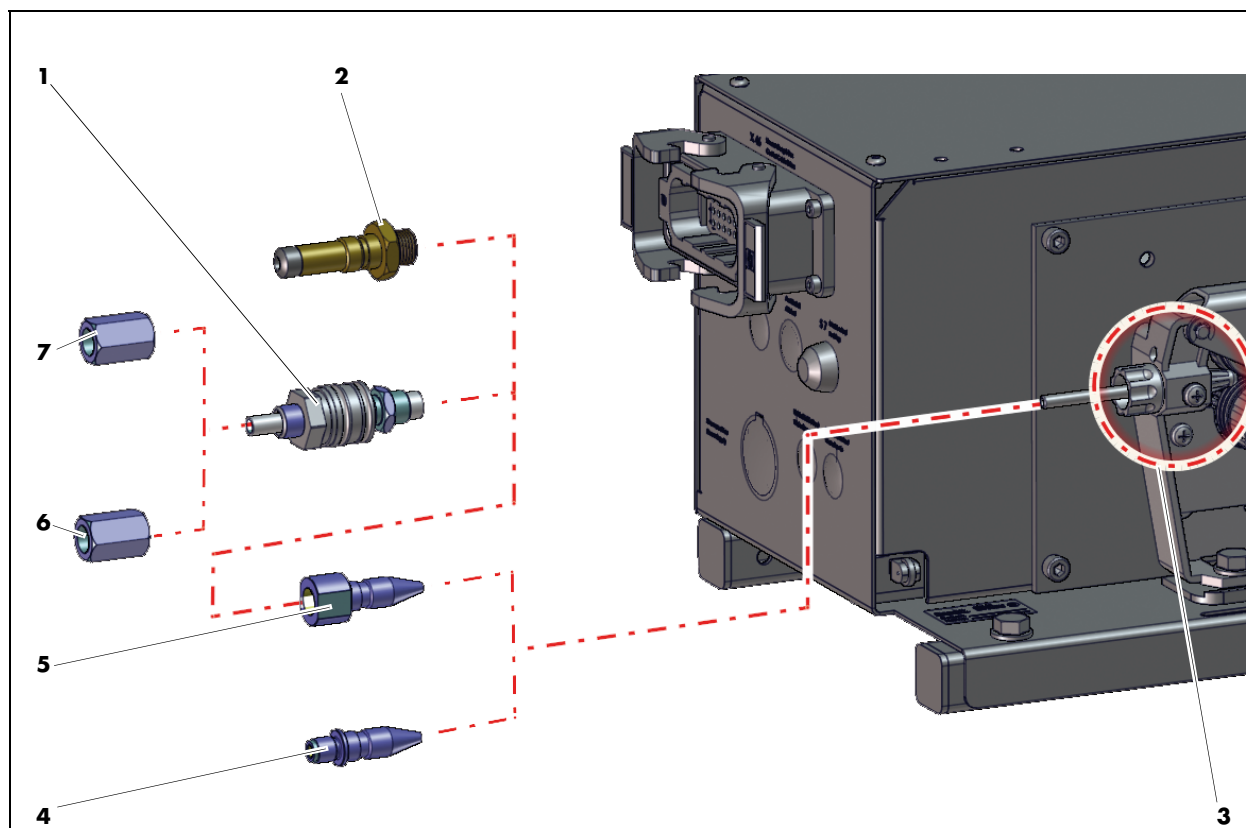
Vue d'ensemble des pièces d'usure M-Drive
